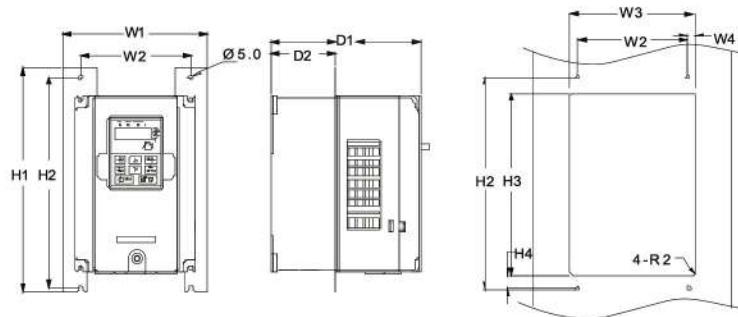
Montaje de Flange para 3PH 220V 4-22kW VFDs
